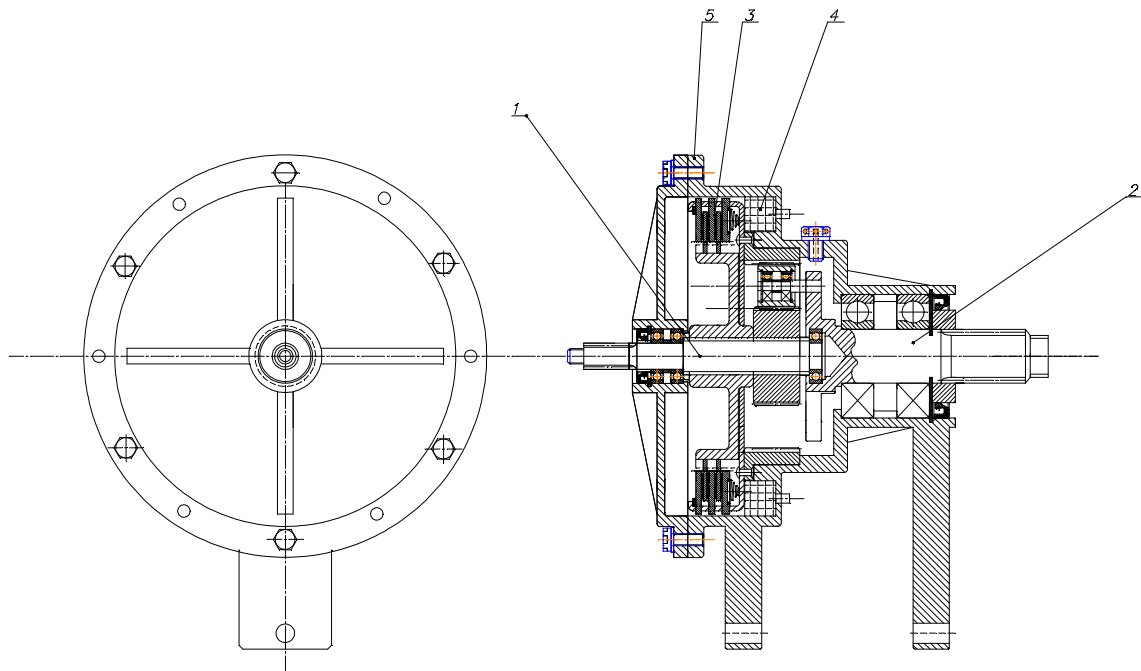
Планетарний редуктор, із змінними передатними числами
